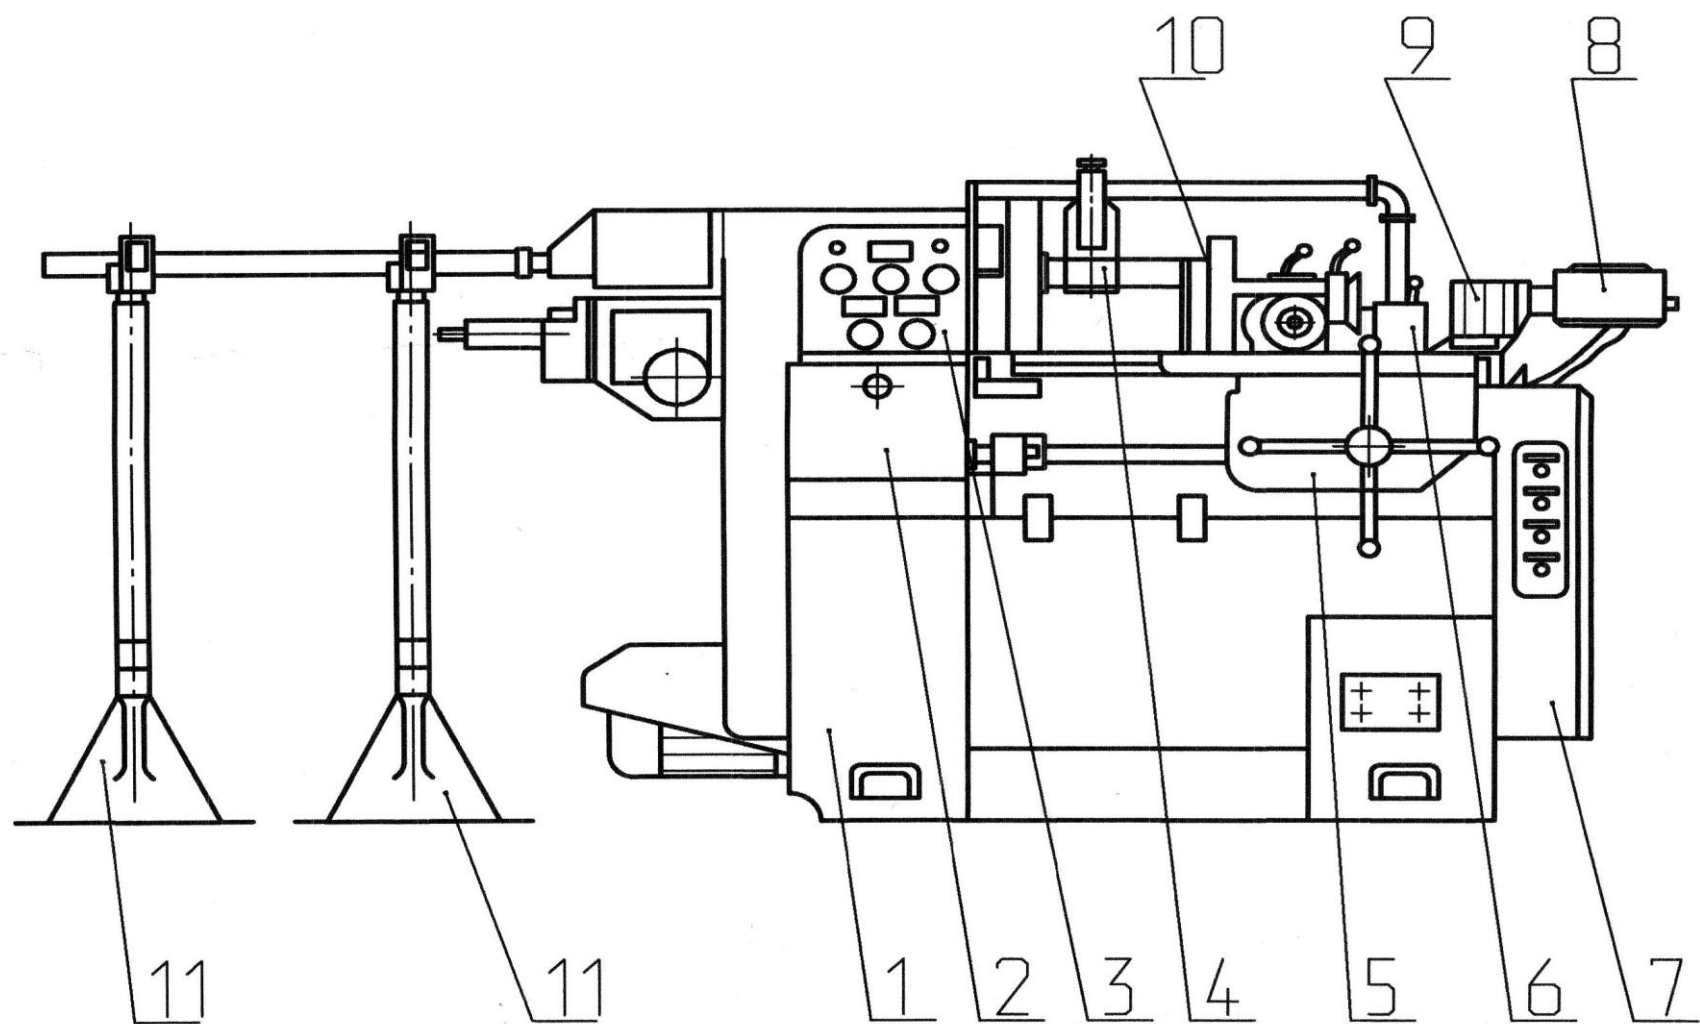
Основные части и органы управления токарно-револьверного станка модели 1Г325
